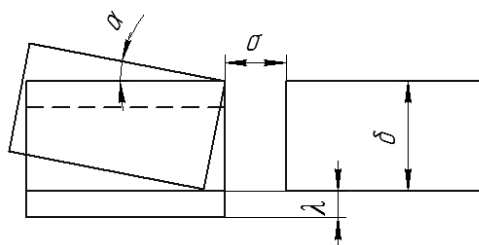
Погрешности сборки под сварку стыкового соединения [29]
